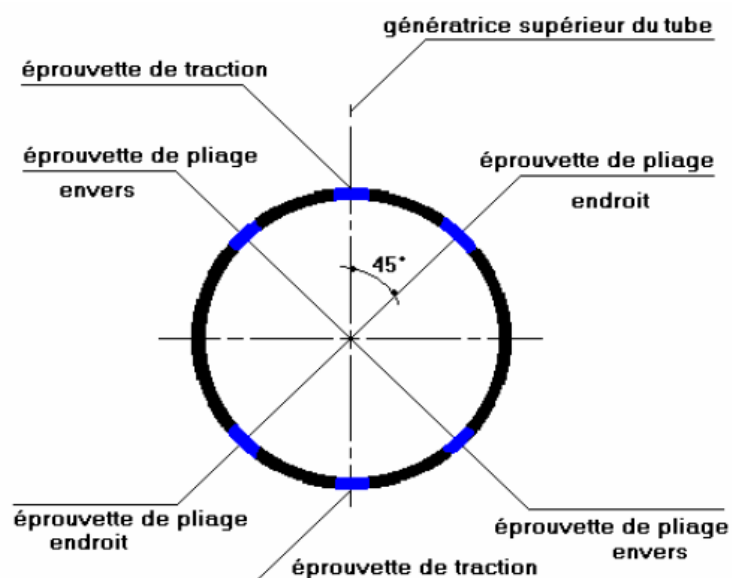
Méthode de prélèvement des éprouvettes sur des tubes soudés.
